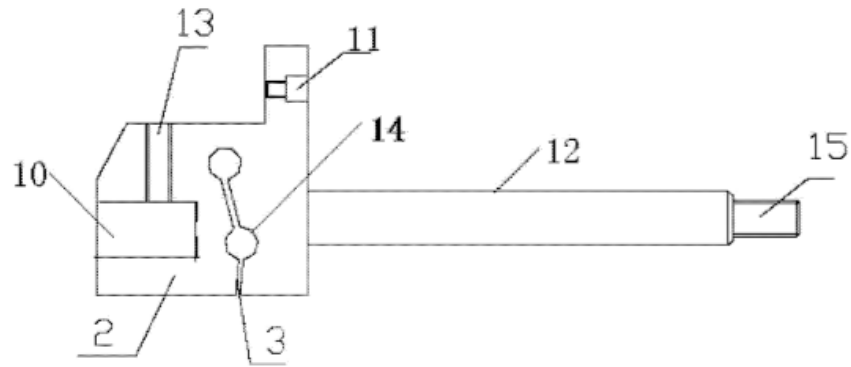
Пристрій для кріплення інструменту [7]
